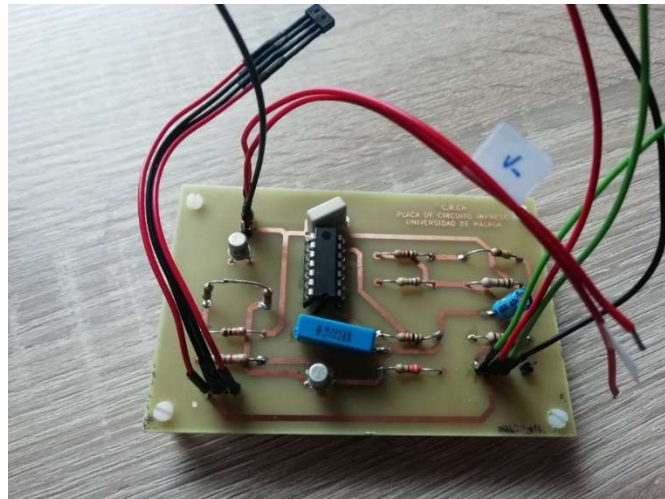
Placa de circuito impreso con los componentes soldados
